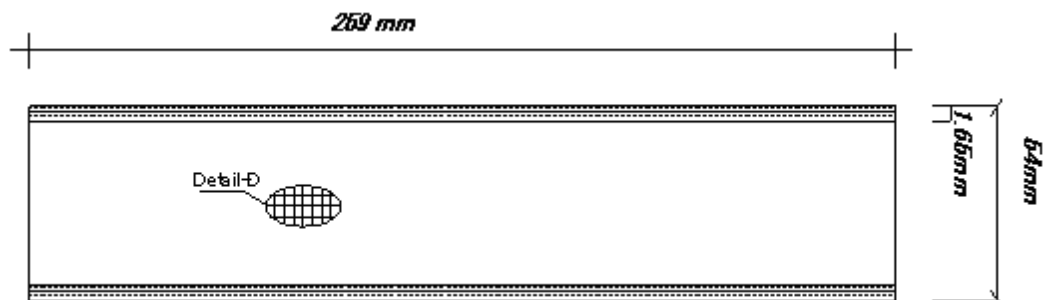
Схема расположения образцов для одноосного растяжения на трубной заготовке.
